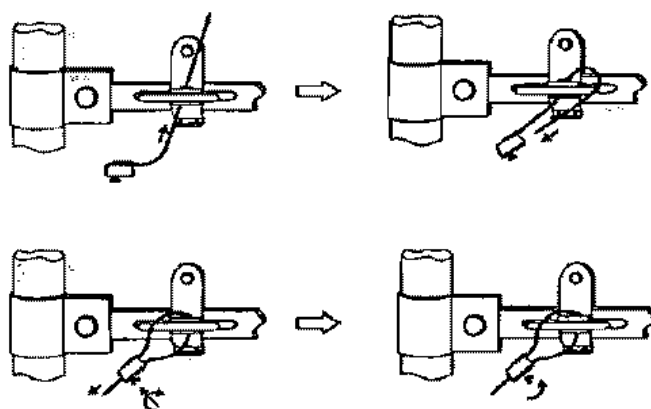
Способ установки ЗПУ «Спрут-777М» на вагон или контейнер
